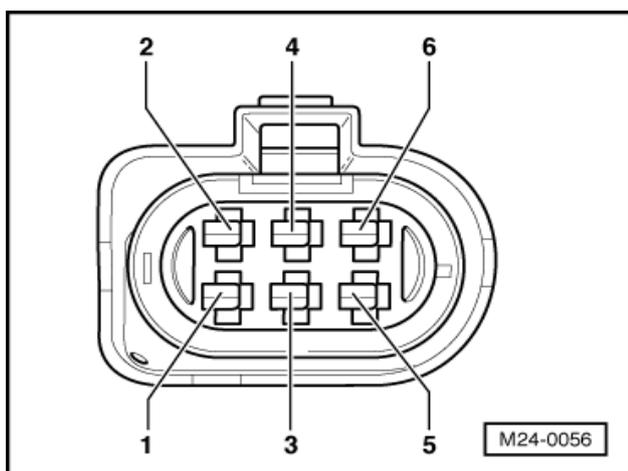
Conector de 6 contactos del lado hacia UCE motor.
